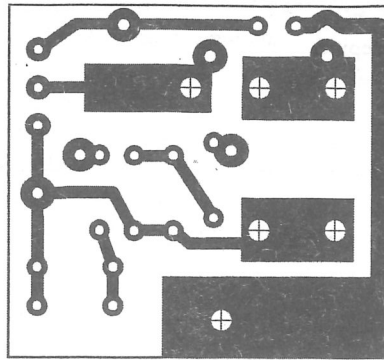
Placa 2; desenul cablajului, vedere dinspre fața placată (50 x 47 mm).
